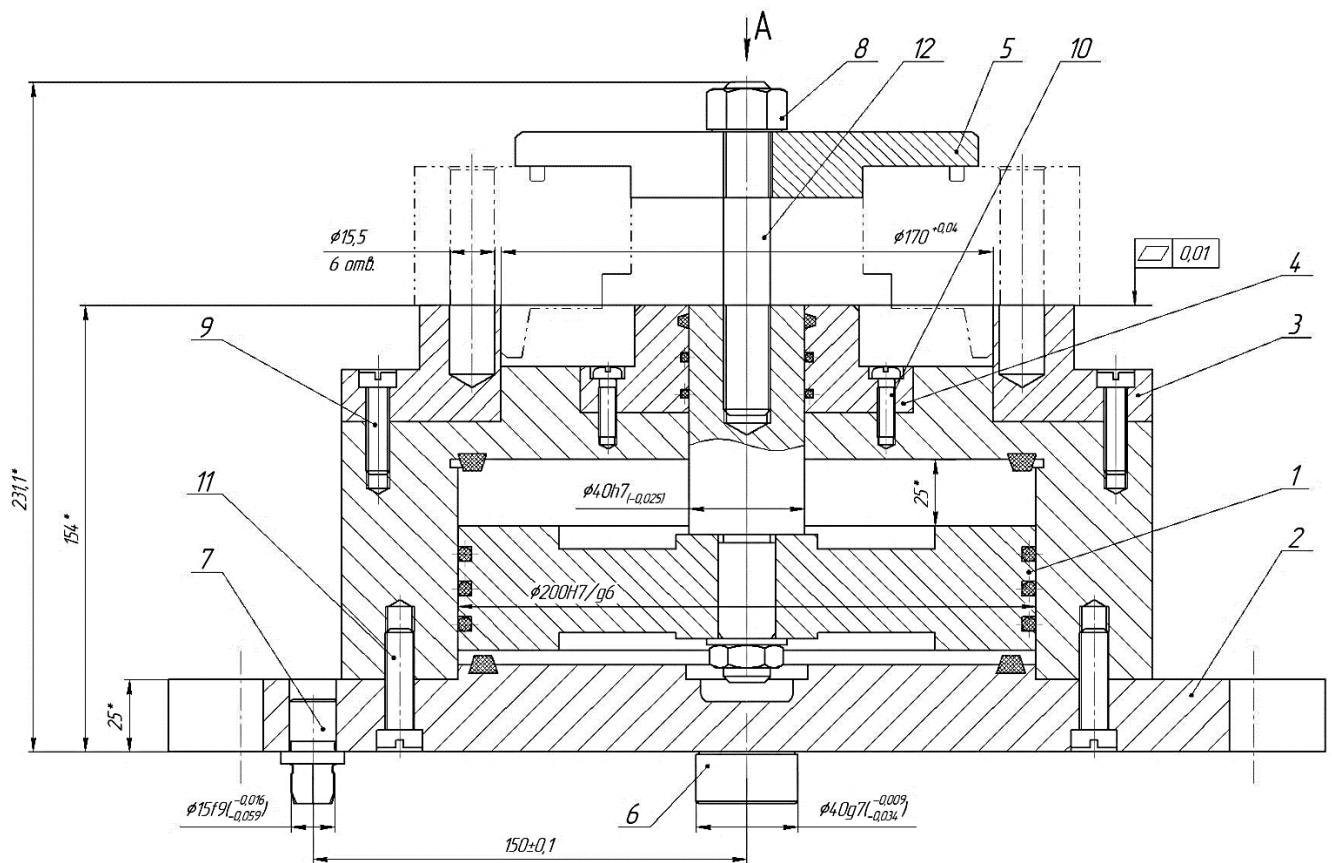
Ескіз пристосування для комплексної обробки
